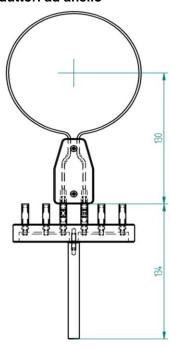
Dimensioni dei conduttori ad anello montati sull'asta di supporto per elementi a spina (1018449)
